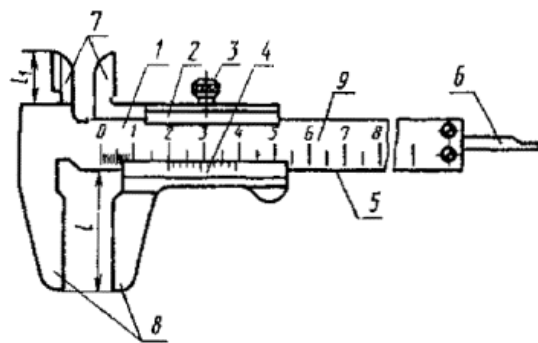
Двусторонний штангенциркуль с глубиномером
